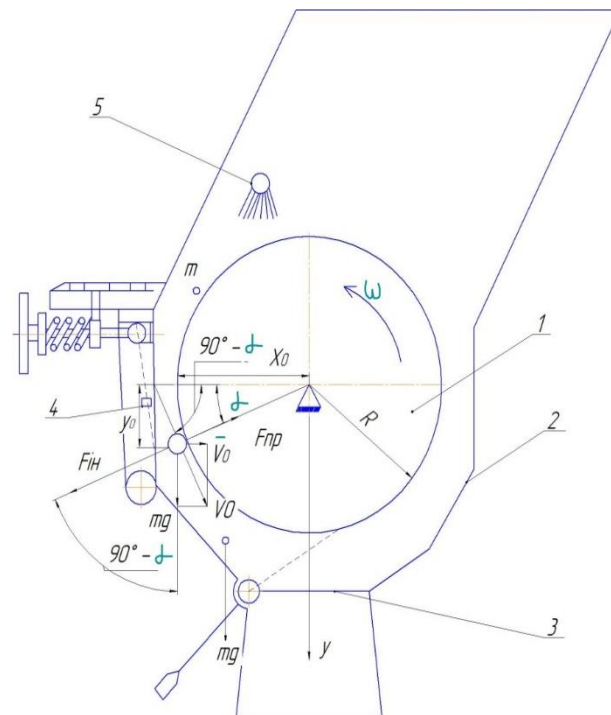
Рух частинки компонентів по поверхні місильного барабана: 1 – рифлений місильний барабан; 2 – багатогранна робоча камера; 3 – шибєр для вивантаження тіста; 4 – патрубок для вивантаження; 5 – пасивний вібраційний пристрій; 6 – нагнітальний пристрій
